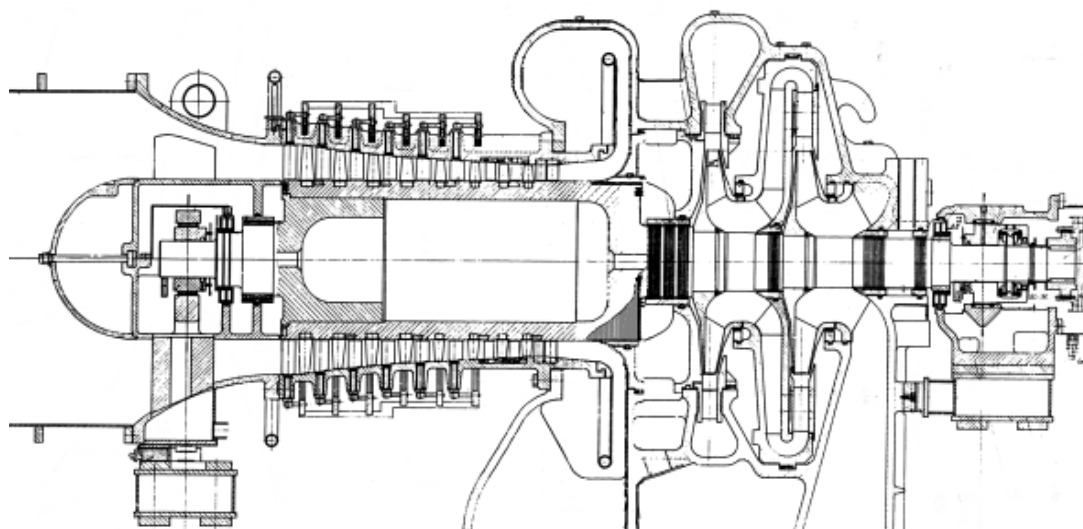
Осецентрибежный компрессор КО-3000 (Невский завод) для блоков разделения воздуха с промежуточным охлаждением между осевой и центробежной частью (лопатки направляющих аппаратов осевого компрессора – поворотные).
